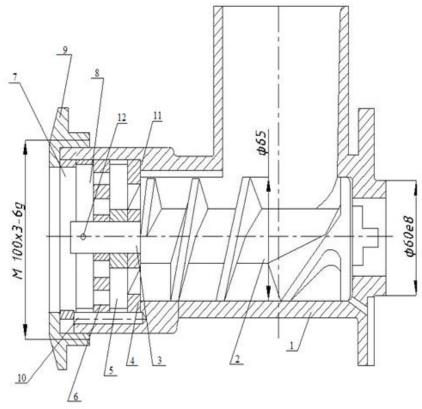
Схемы установки режущего инструменты в системе Энтерпрайз
